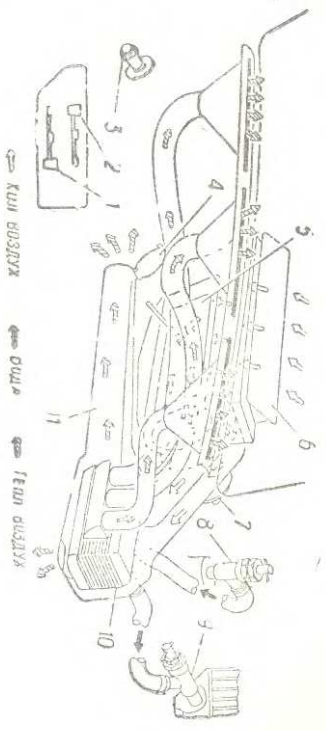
Отопление и вентиляция кабины и обдув ветрового стекла:
